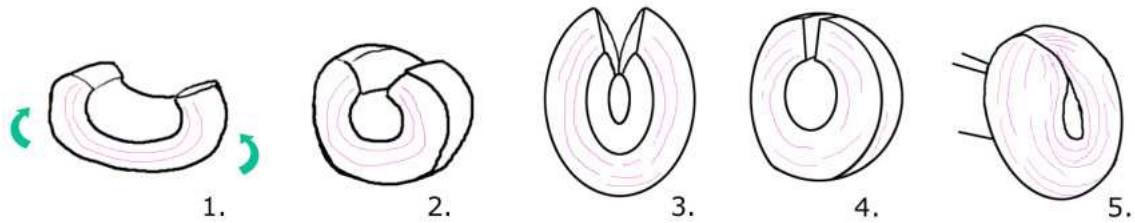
Procédé par pliage et soudage séparé. Dessin F. Cognot.
